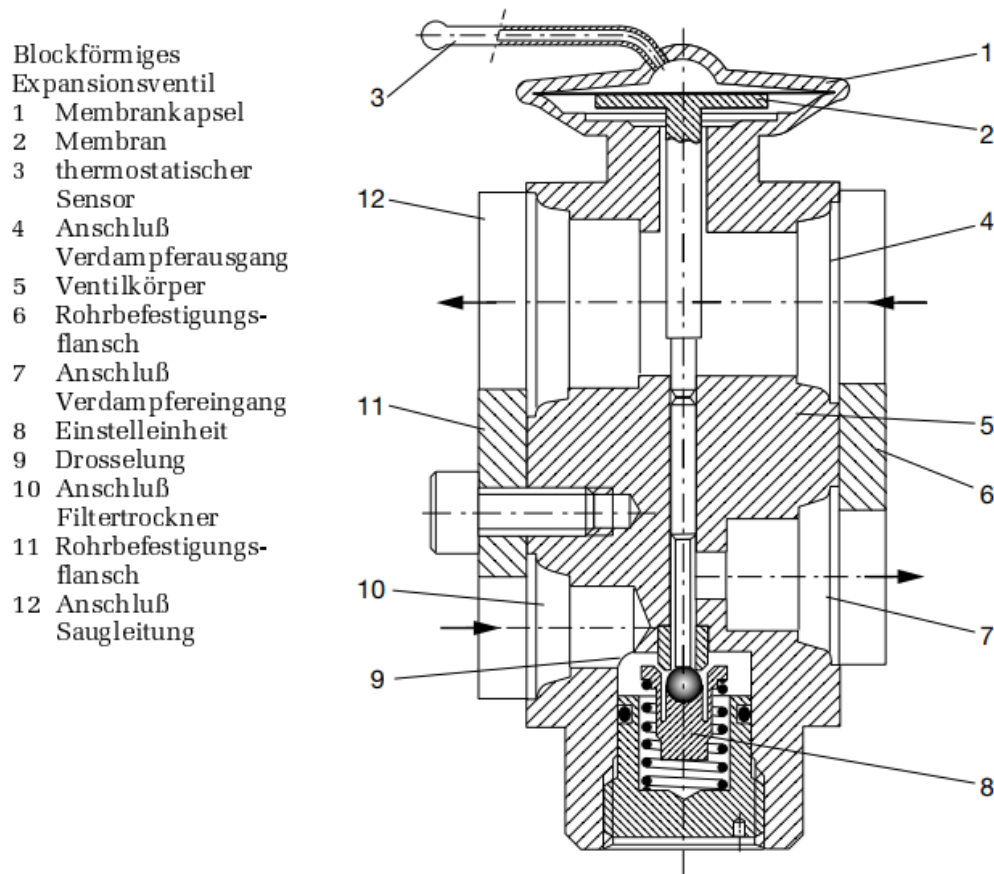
Expansionsventil mit Bauteilbeschreibung [5]
